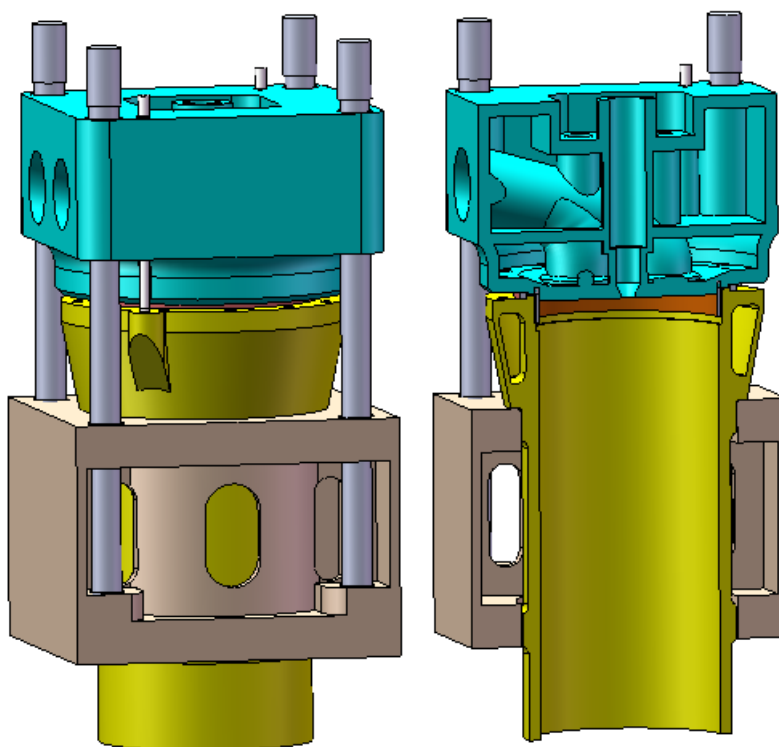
Твердотельная модель сборки блока, цилиндра и крышки
